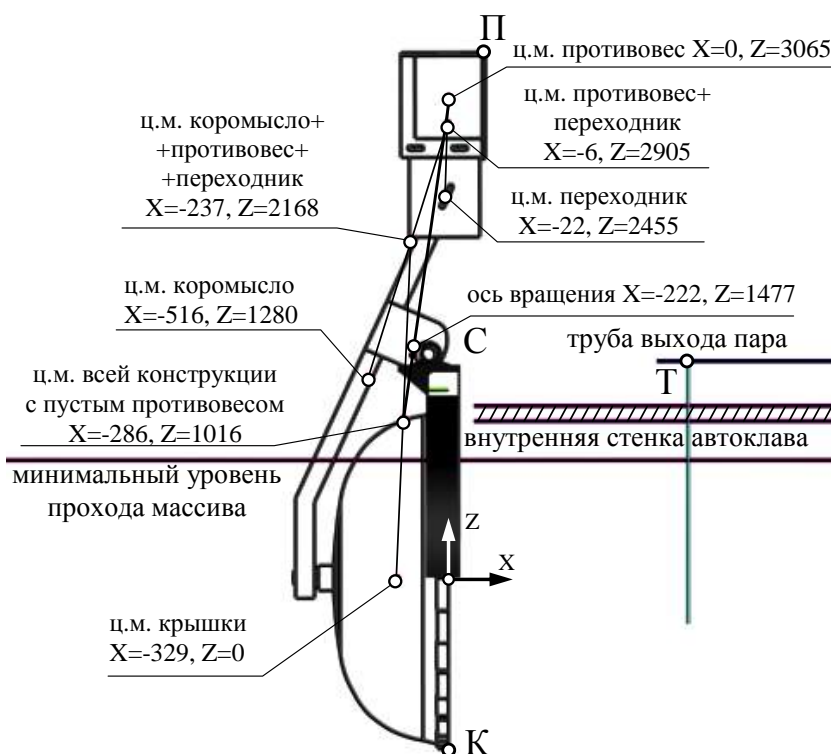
Сетка положений центров масс звеньев конструкции РУ открытия автоклава
